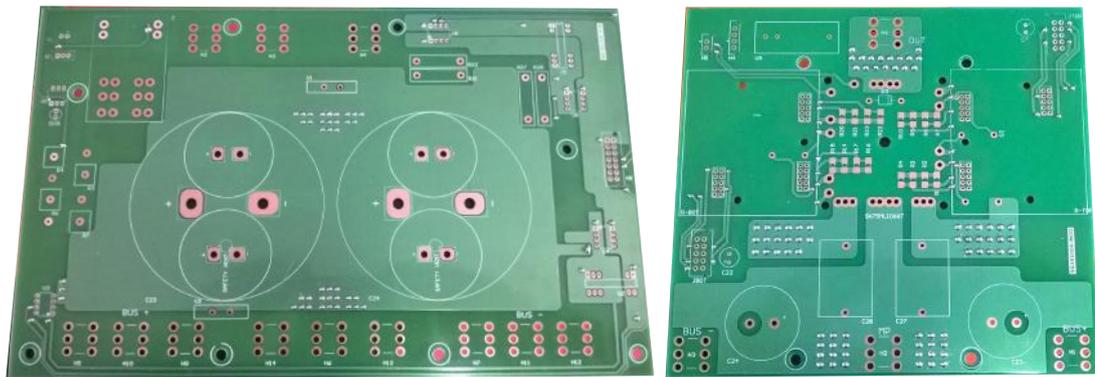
PCB Banco de Capacitores (izquierda)- PCB Rama Convertidor (derecha)
